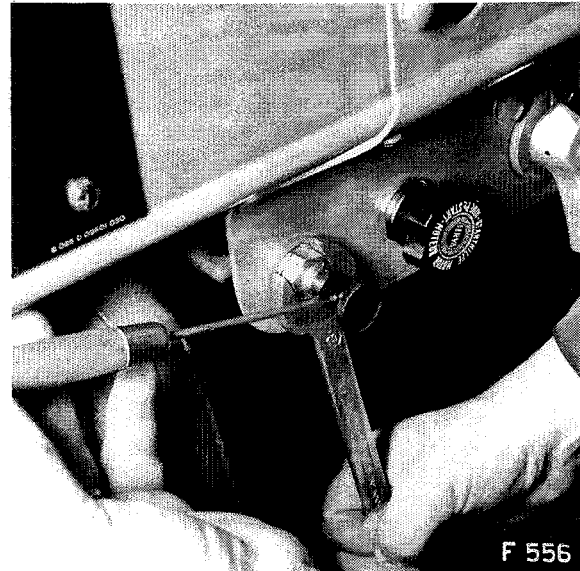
Lösen der Befestigungsmutter und des Handgriffs am Regulierventil für den Scheibenwischermotor.
